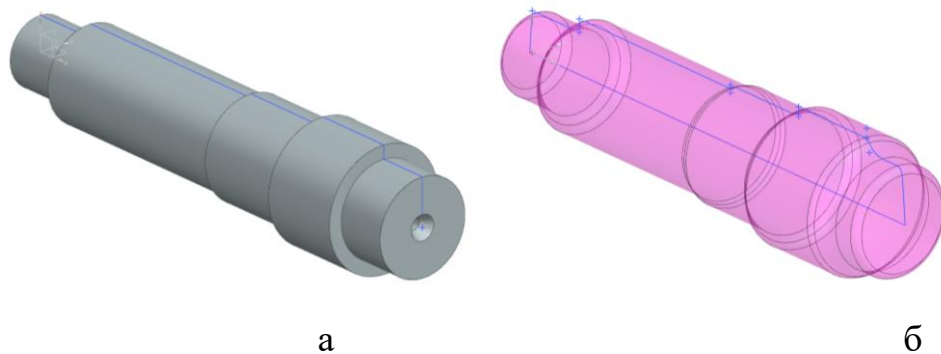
3D зображення деталі після токарної обробки (операція 010) (а) та зображення заготовки (б)
